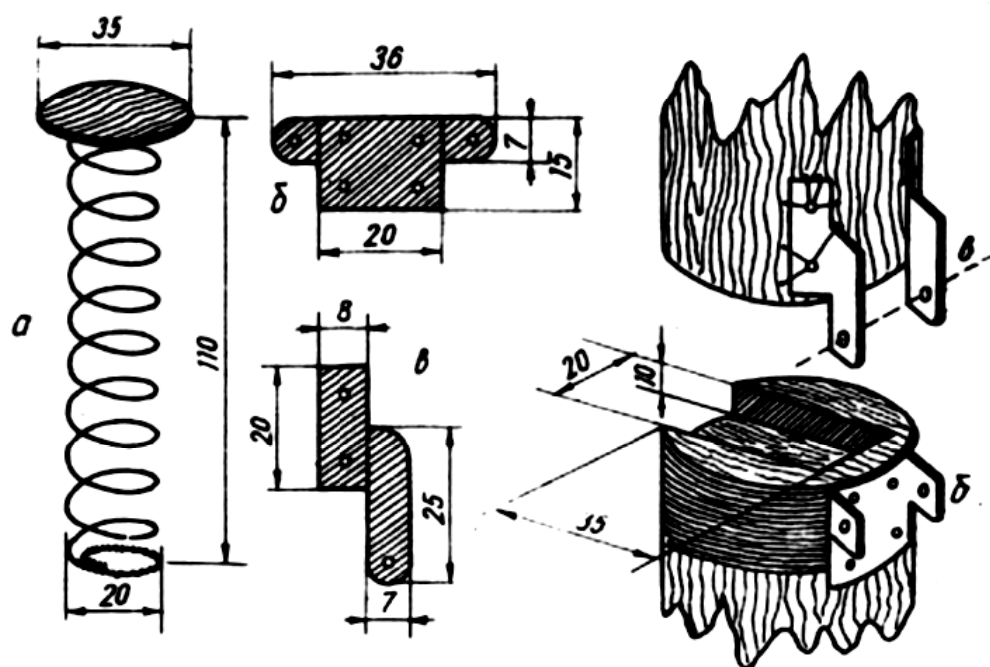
Металеві деталі корпусу та обтічника: а) виштовхувальна пружина; б) вушка від корпусу ракети; в) вушка від обтічника.
